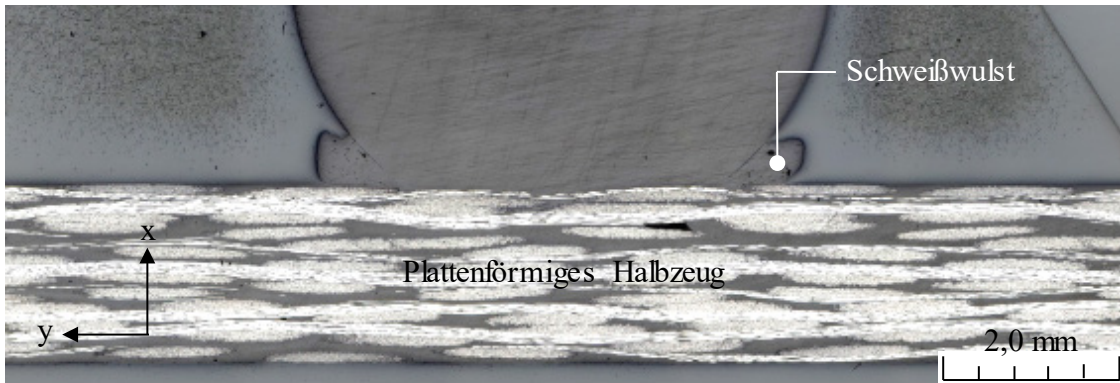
Schliffbild der Schweißverbindung PA6-CF/PA6
